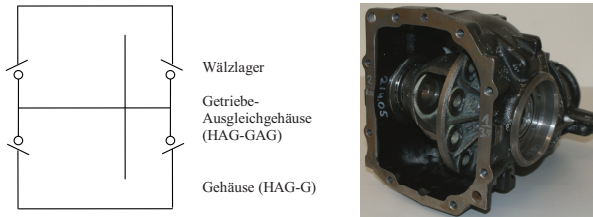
Hinterachsgetriebe-Baugruppe mit Wälzlager (HAG-BGRW)
